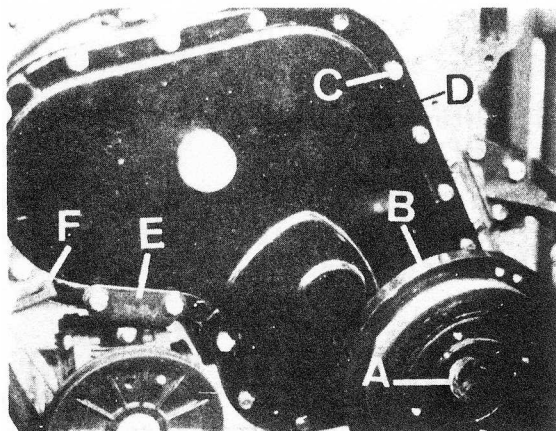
Desmontaje de la tapa de la distribución y damper
